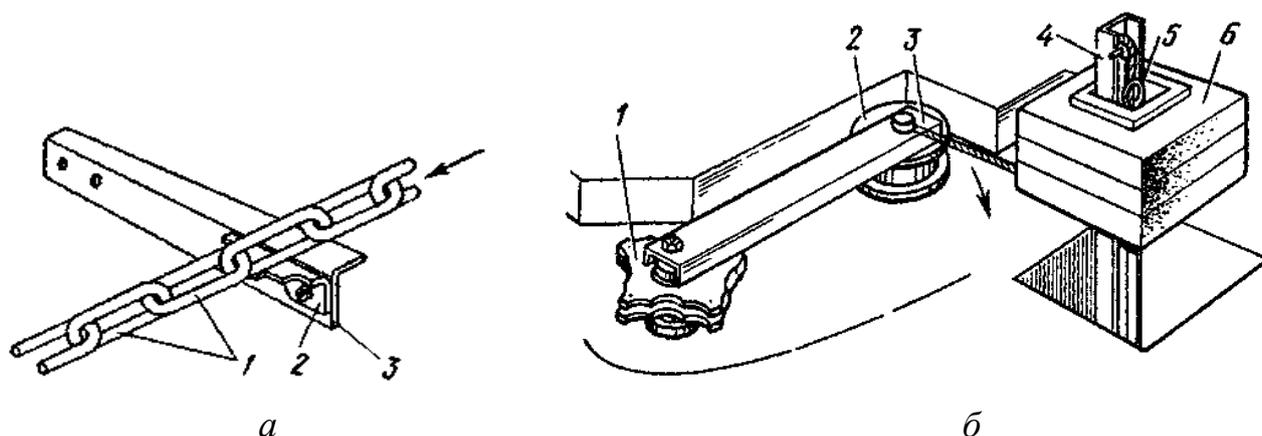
Цепь со скребком (а) и автоматическое натяжение скребкового транспортёра ТСН-160А (б): а: 1 - звено цепи; 2 - кронштейн; 3 - скребок;
